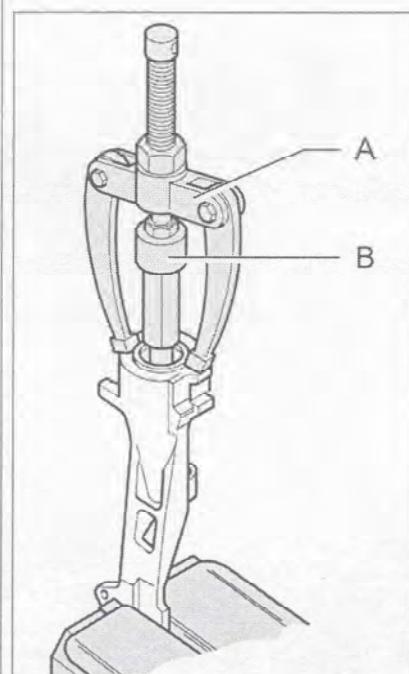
Извлечение шарикоподшипника из поводка рычага включения передачи заднего хода.
